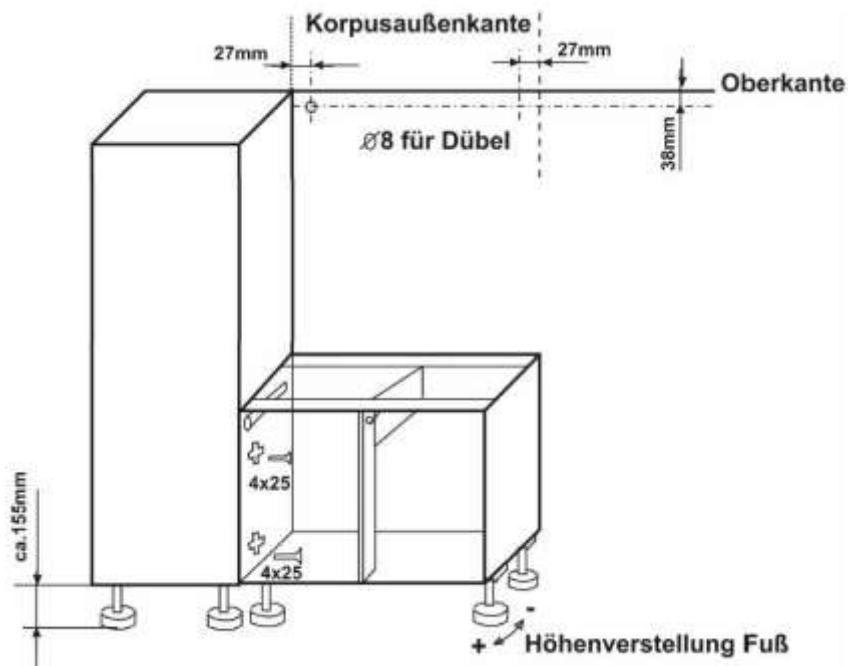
Oberschranksaufhängung und Korpusverschraubung.
